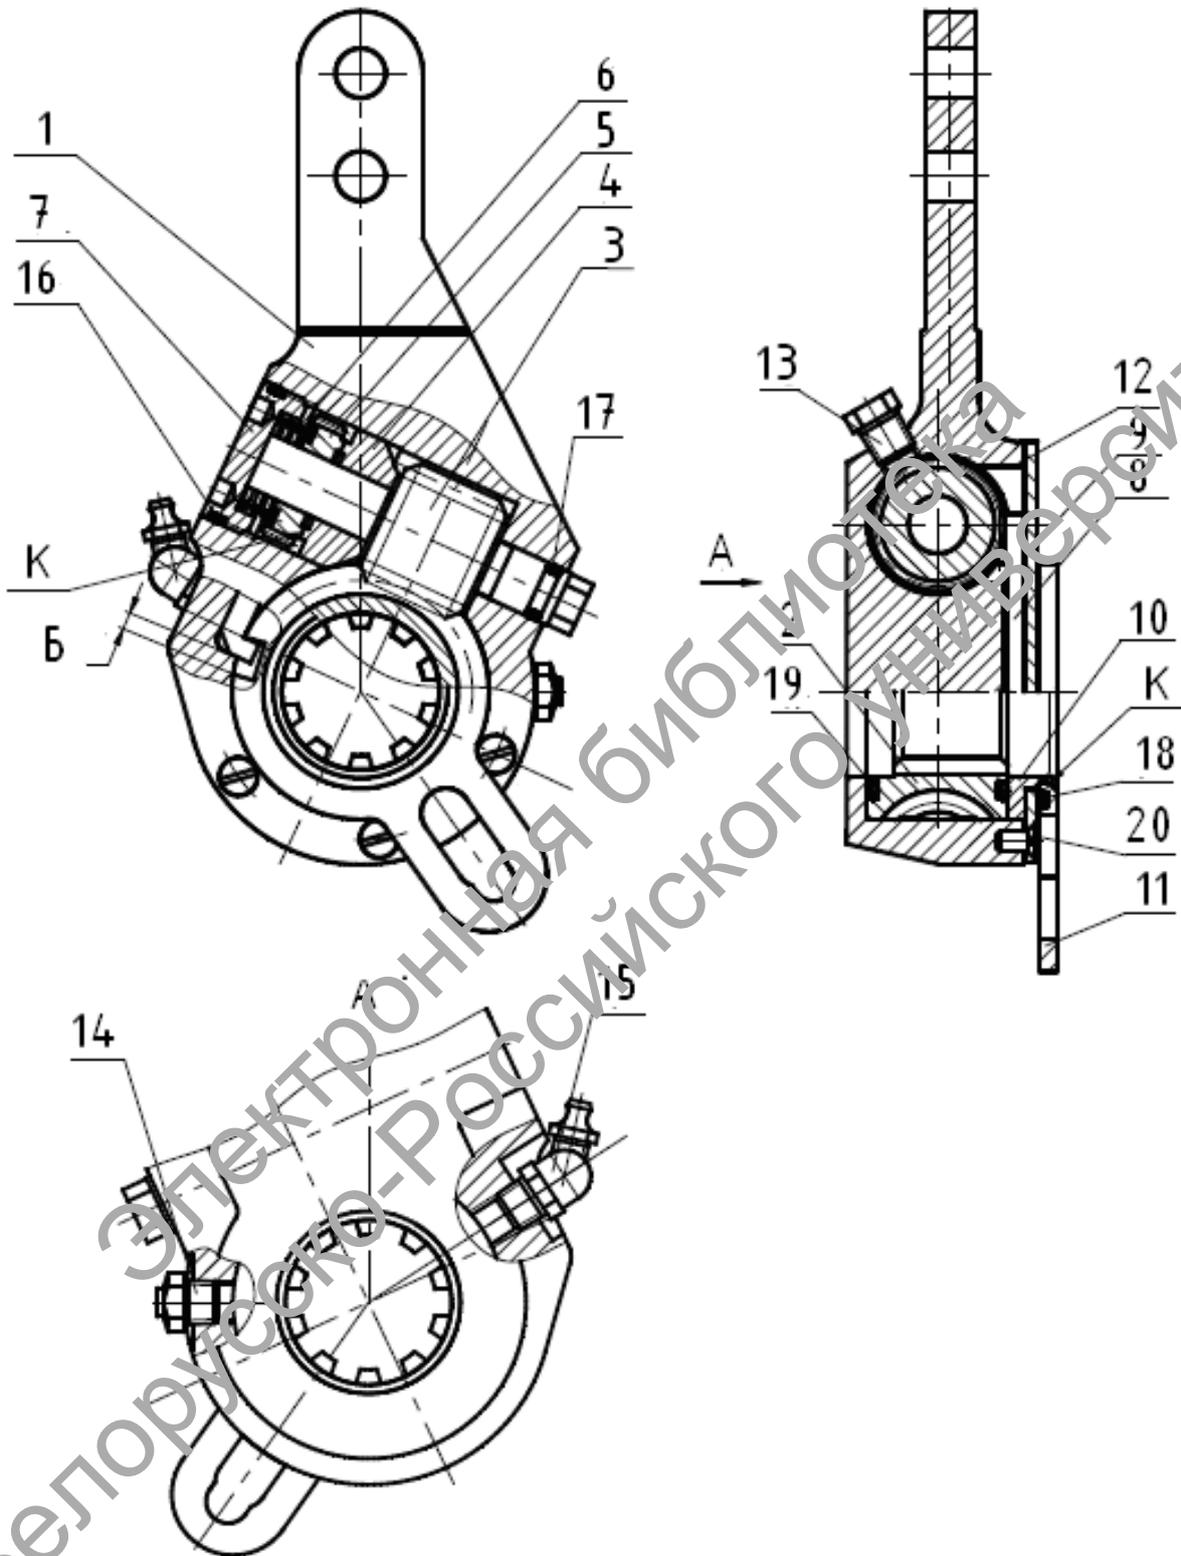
Устройство автоматического регулятора зазора тормозных колодок автомобилей семейства МАЗ: 1 – корпус; 2 – шестерня; 3 – вал червячный; 4 – неподвижная полумуфта; 5 – подвижная полумуфта; 6 – пружина; 7 – заглушка; 8 – толкатель; 9 – крышка; 10 – кольцо управляющее; 11 – поводок; 12 – прокладка; 13 – пробка; 14 – предохранительный клапан; 15 – масленка; 16, 17, 18, 19 – кольца; 20 – винт
